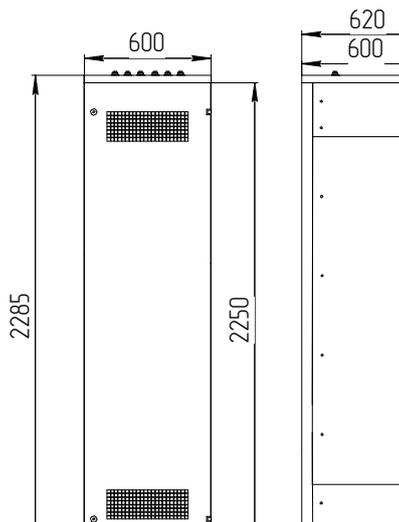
Габаритный чертеж шкафа аккумуляторного СУЭП-2 А1
